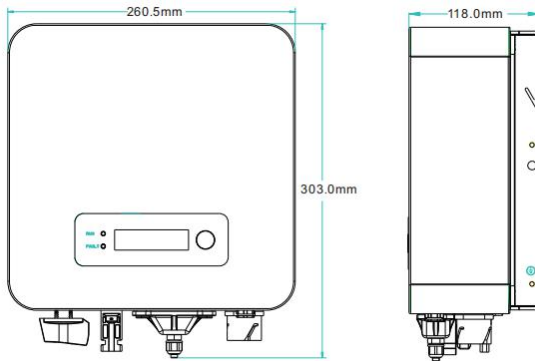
Dimensions vue de face et vue de gauche du SOFAR 3300TL-G3
